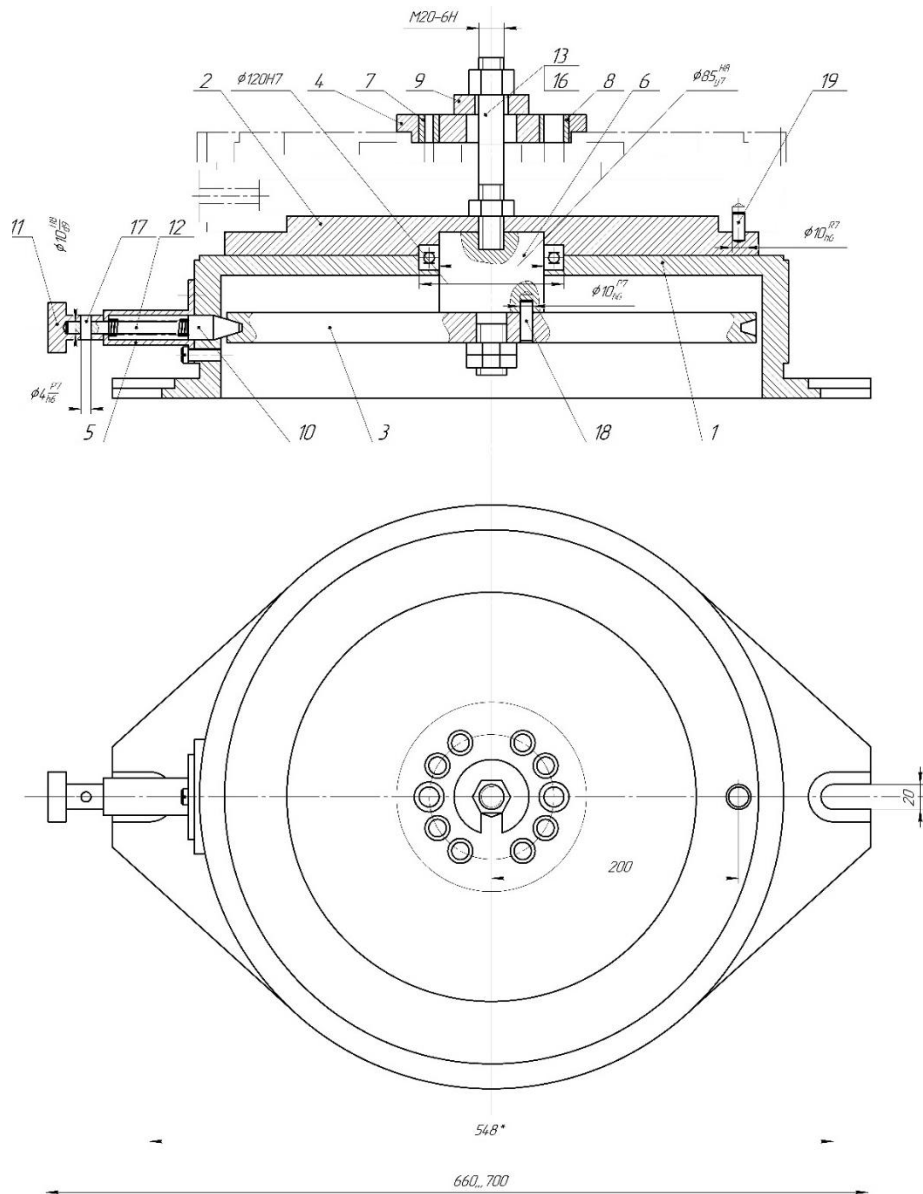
Пристрій для закріплення маховика: 1 – остов; 2 – стіл; 3 – ділильний диск; 4 - ; 5 – корпус; 6 – вал; 7, 8 – втулки; 9 – ; 10 – фіксатор; 11 – ; 12 – пружина; 13 – гайка; 14 – ; 15 – гвинт; 16 – шпилька; 17 – підшипник; 18 – ; 19 – ; 20 – штифт;
